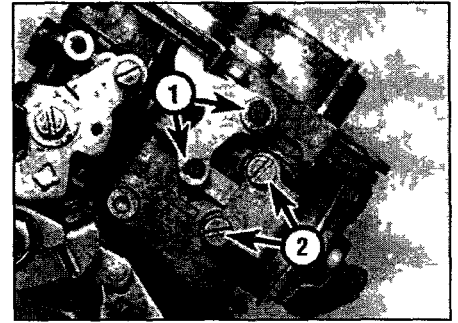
Снимите фиксаторы (1) и отсоедините поворотный рычаг вакуумного привода от крышки карбюратора
